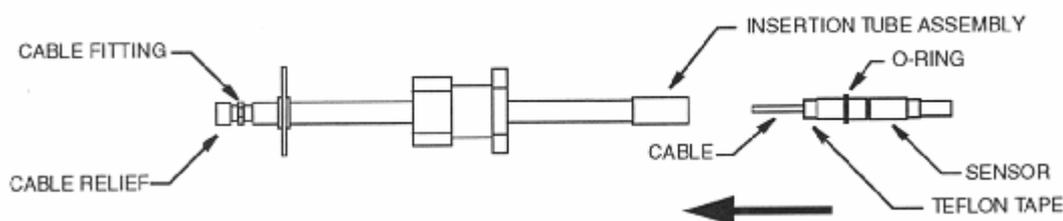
Instalación del sensor en el conjunto de tubo de inserción
